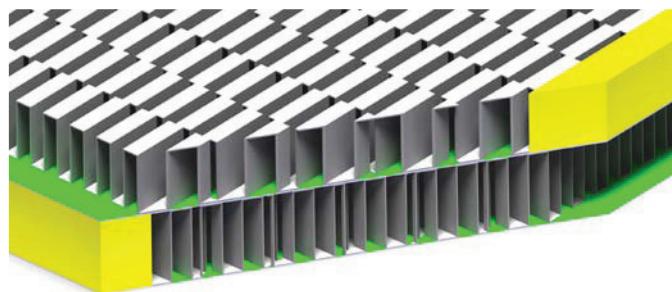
Перекрестное расположение поверхностей ПлР. Начальный этап сборки
